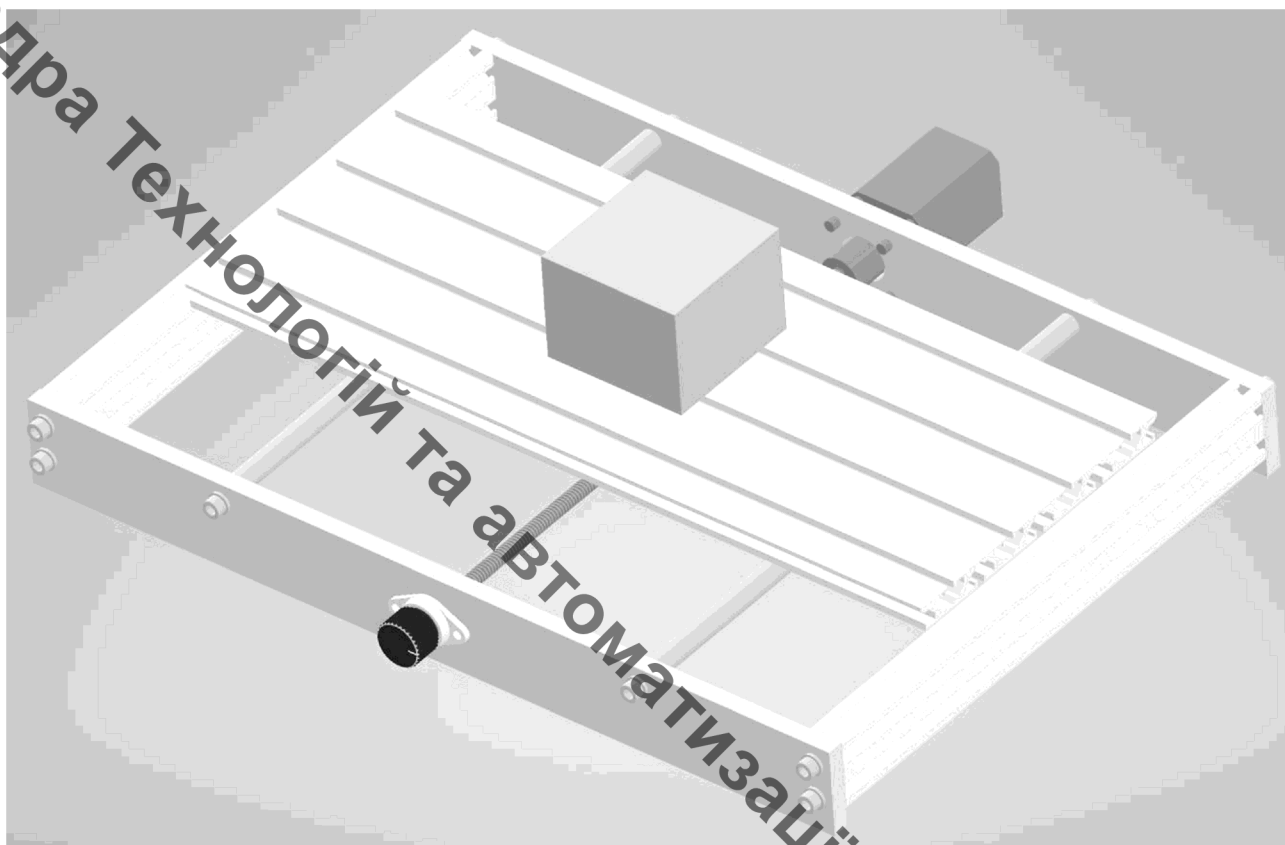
Портал фрезерно-гравірувального верстата з ЧПК
